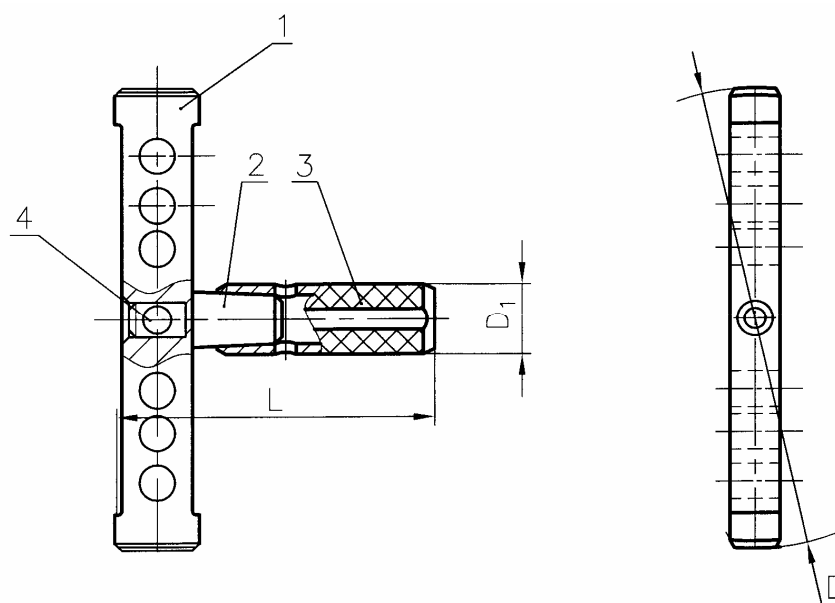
Гладкий проходной неполный калибр-пробка:
